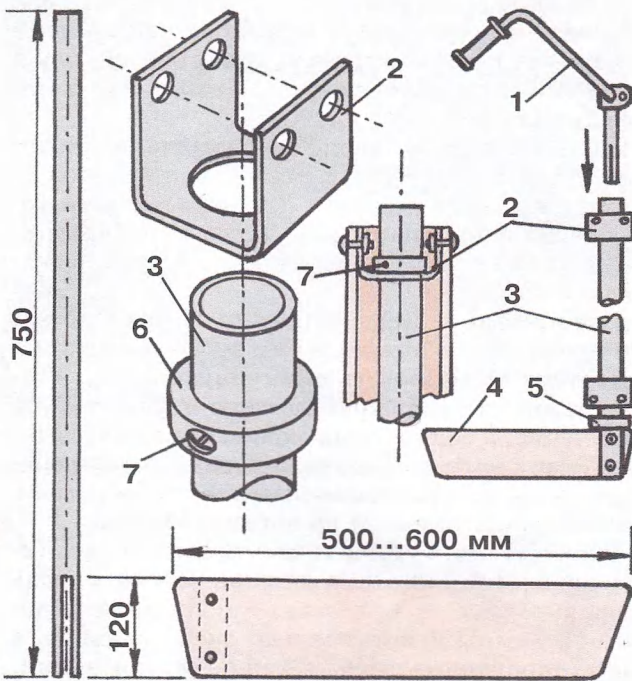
Детали рулевого управления: 1 — руль от велосипеда; 2 — скоба (2 шт.); 3 — колонка руля; 4 — перо руля; 5 — пластиковая шайба; 6 — металлическая шайба; 7 — контрольный винт.
